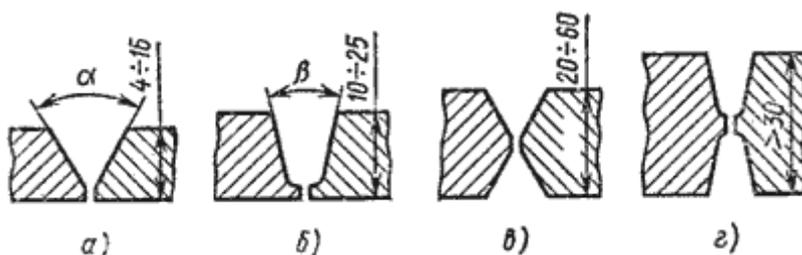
Формы подготовки кромок под сварку:
